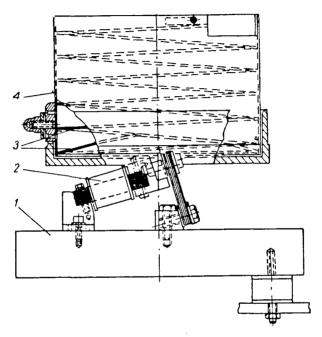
Автоматический вибрационный питатель для поштучной подачи изделий в обрабатывающие станки:
